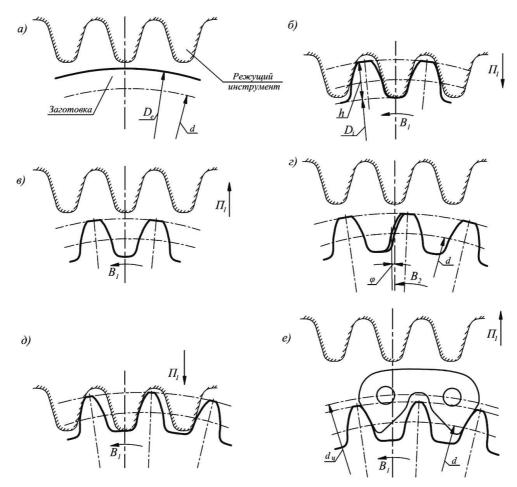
Этапы нарезания зубьев эвольвентной звездочки стандартным режущим инструментом:
